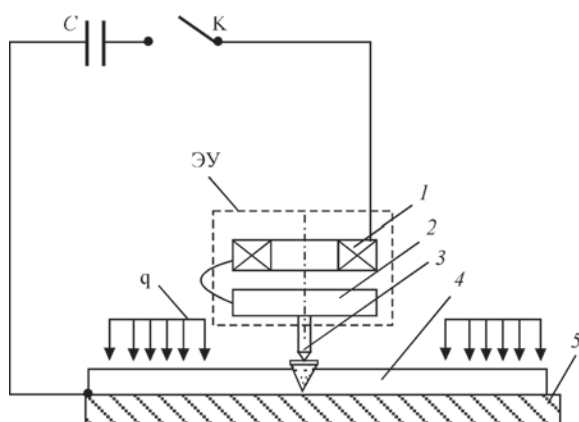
Схема ЭДО сварных соединений (C — емкостной накопитель энергии; K — силовой ключ; q — фиксирующая нагрузка); 1 — индуктор; 2 — диск; 3 — электрод; 4 — образец; 5 — сборочная плита
